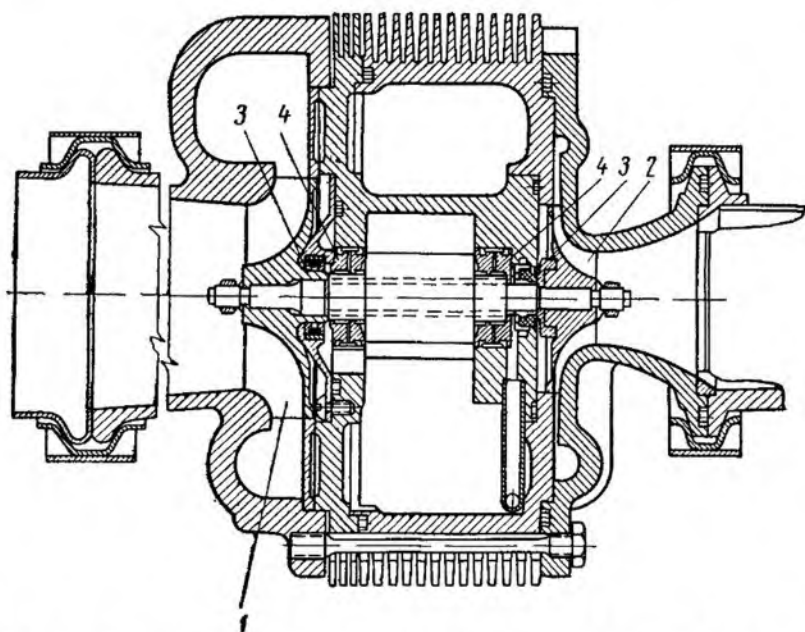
Высокооборотный фреоновый компрессор с приводом от воздушной турбины:
